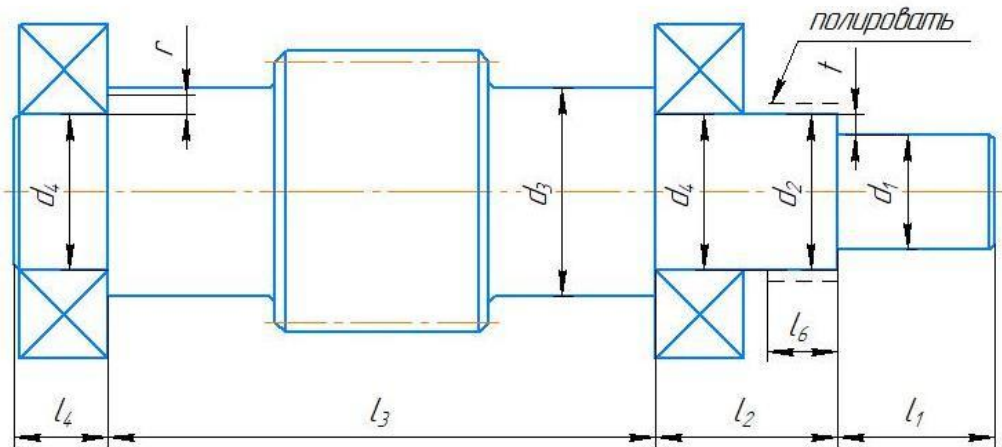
Быстроходный цилиндрический вал
